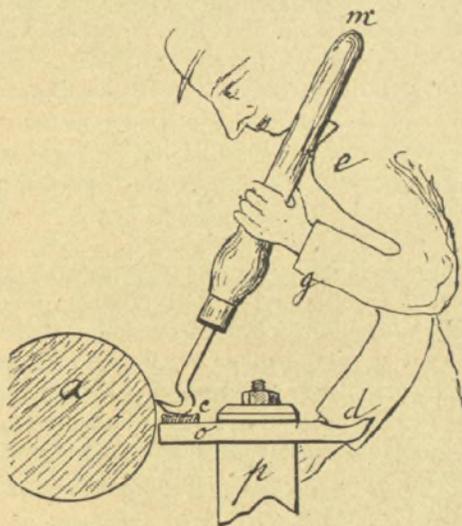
Emploi de la plane à main ou des crochets de tour avec manche en bois, pour le finissage et le polissage des pièces dégrossies.
